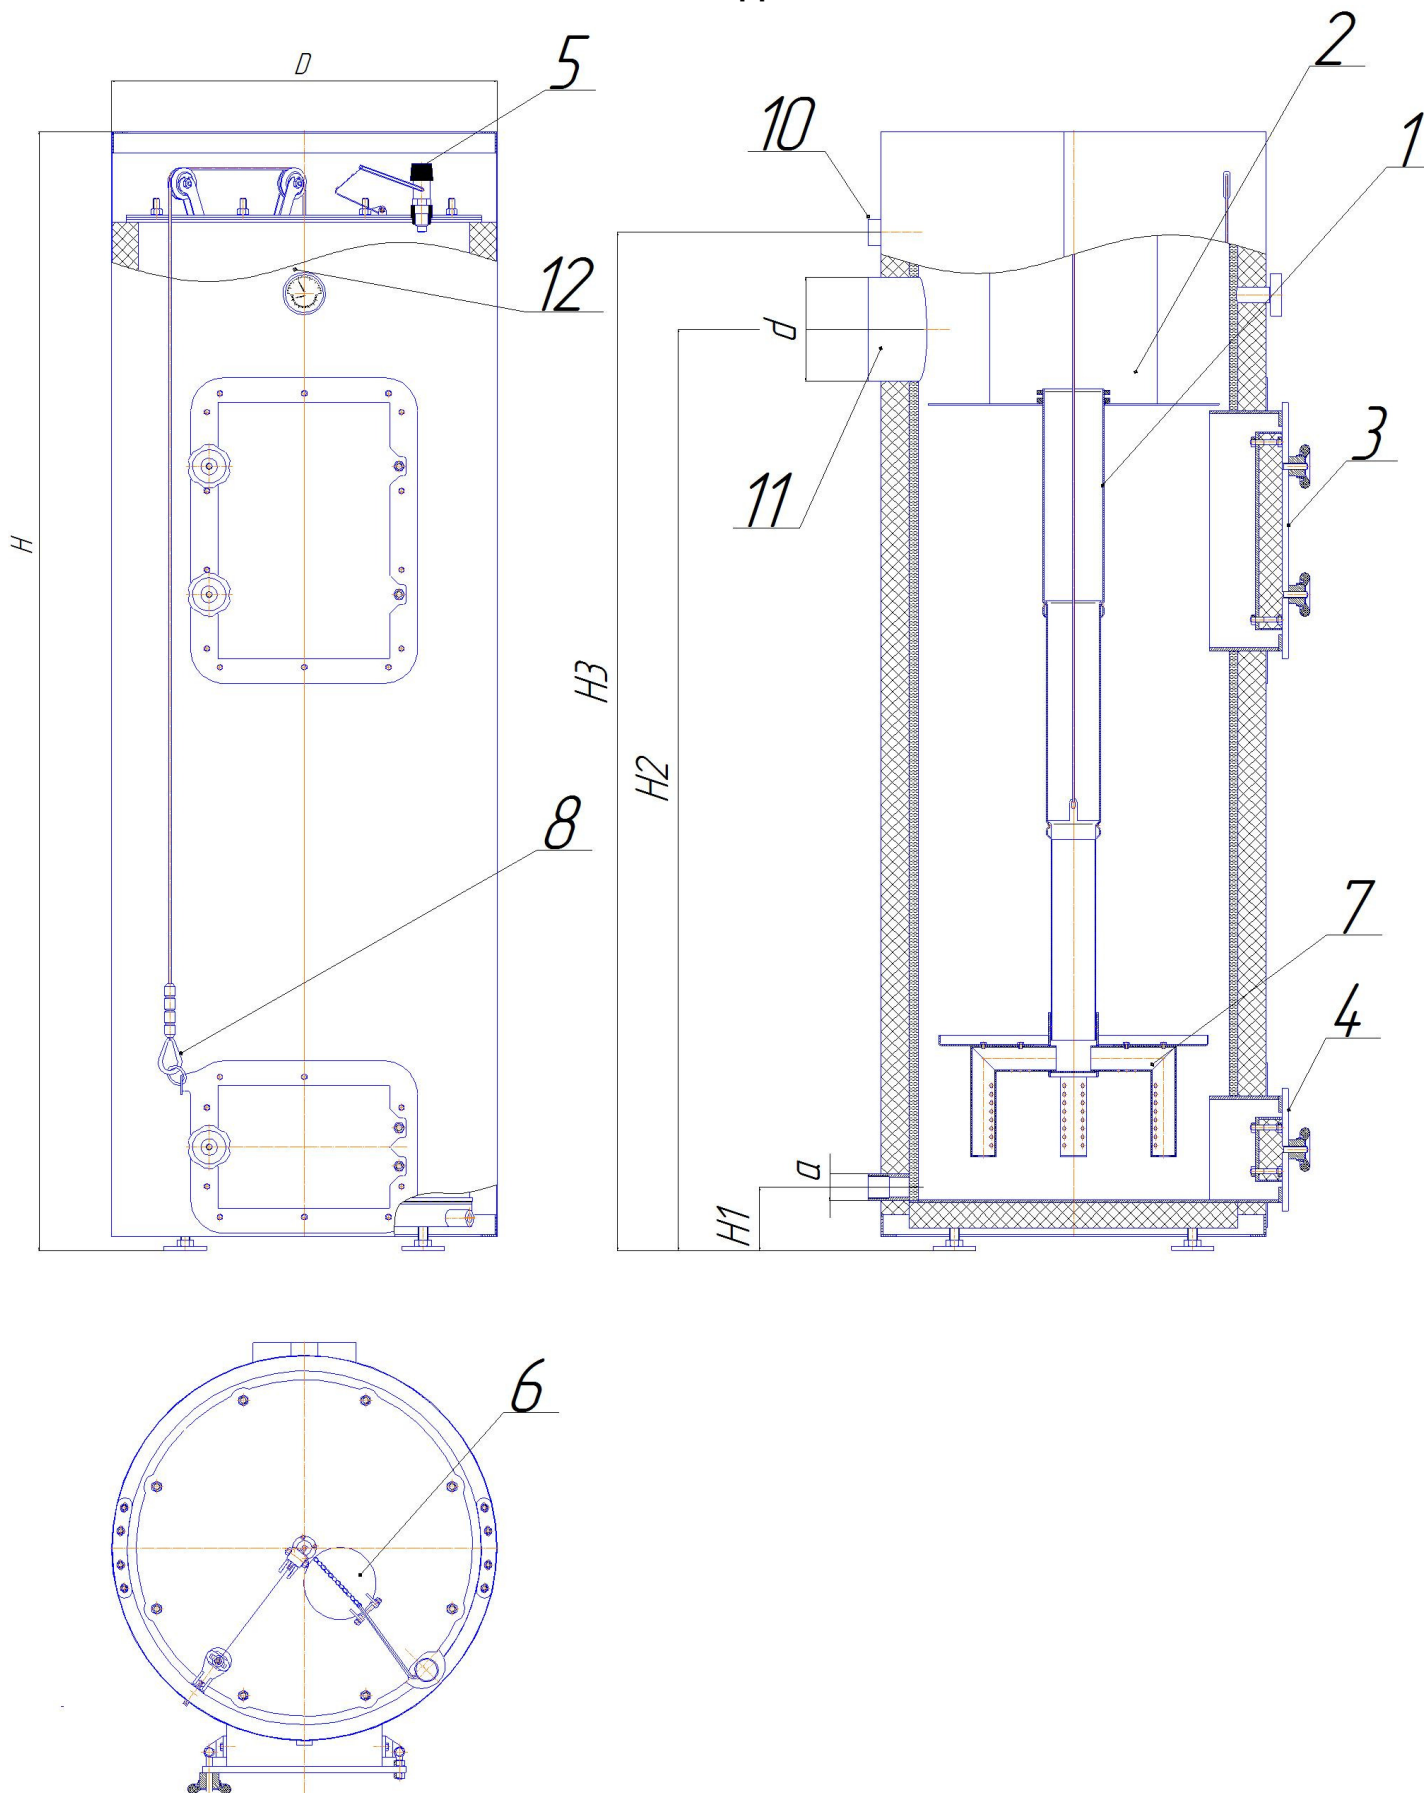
Габаритные и присоединительные размеры версии "KBp"
